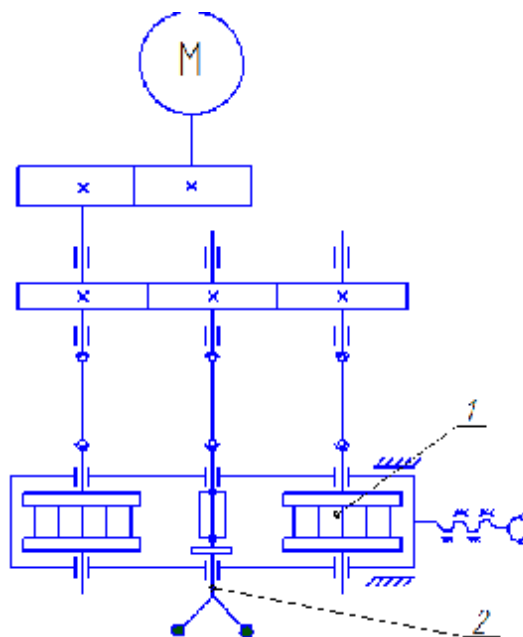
Кинематическая схема стана для накатки шестерен:
